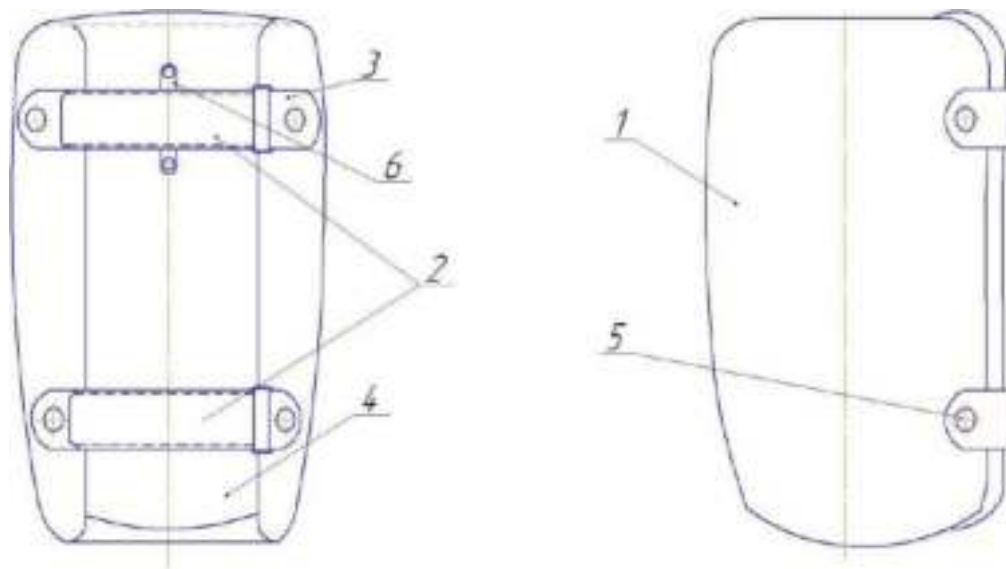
Загальний вигляд безшарнірного ортеза на стегно:
